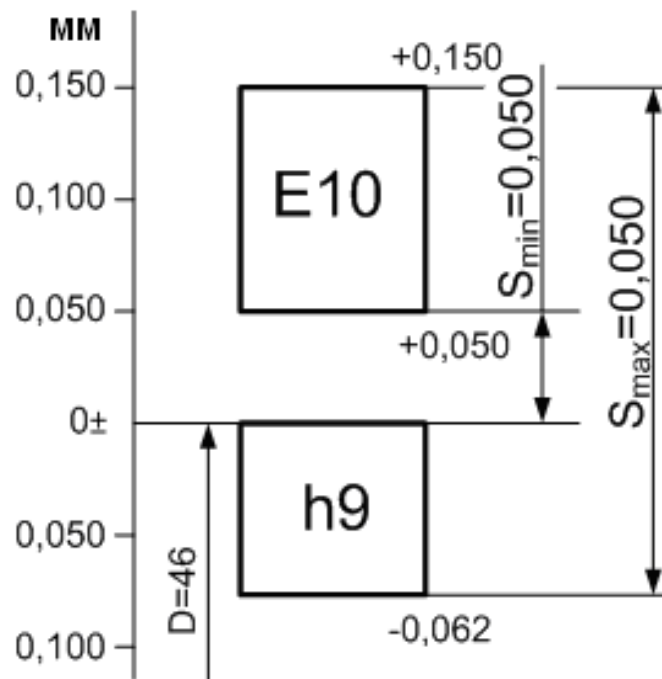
Схема розташування полів допусків деталей з'єднання Ø46E10/h9
